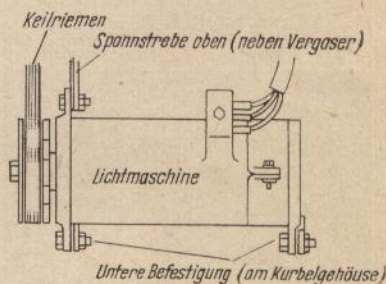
Dreipunktbefestigung der Lichtmaschine
